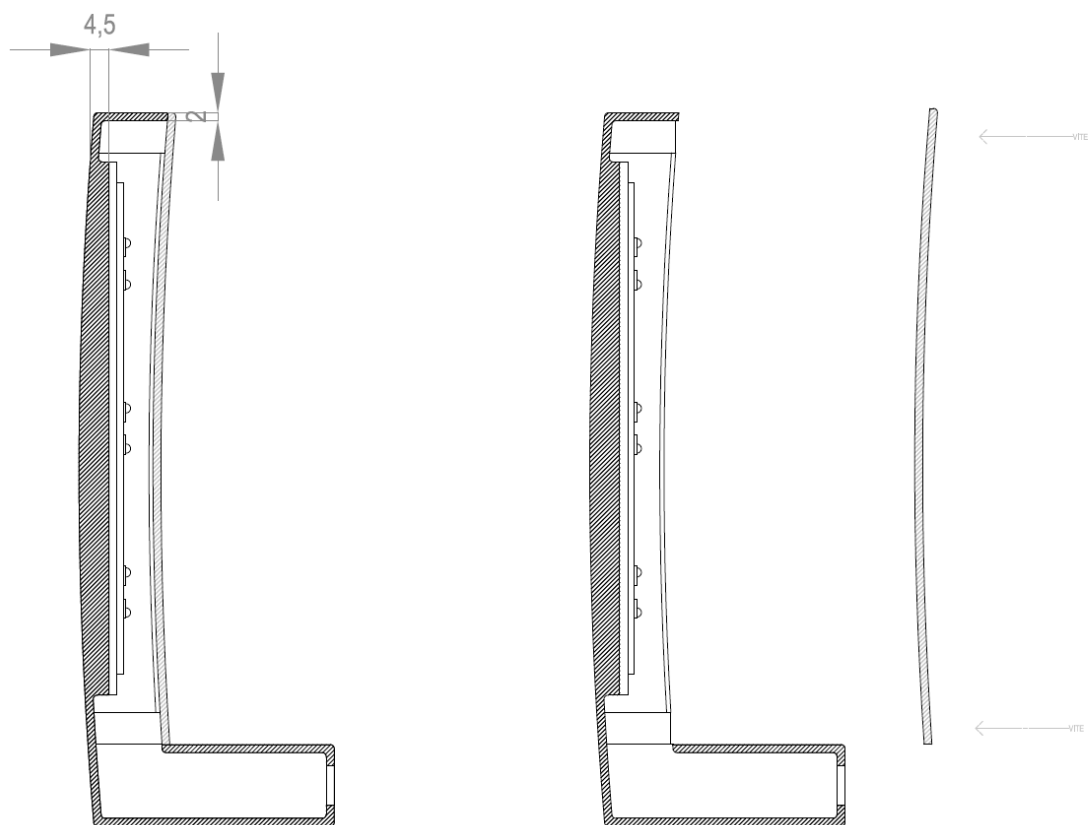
Vista in sezione prospettica del modulo applique a parete
